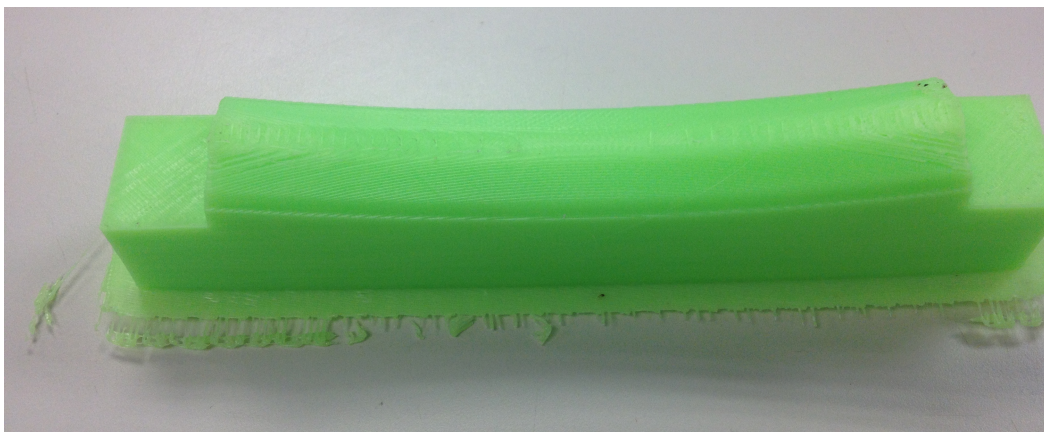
Experimento 2. Resultado del molde interior mediante impresión 3D. (Fuente: Propia)
